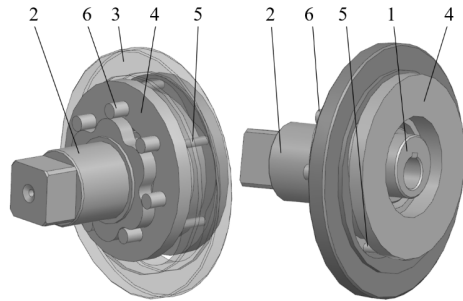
Циклоидально-цевочная передача: 1 – ведущий вал; 2 – ведомый вал с центральным циклоидальным колесом; 3 – корпус с центральным циклоидальным колесом; 4 – сателлит; 5, 6 – два венца сателлита с роликами
